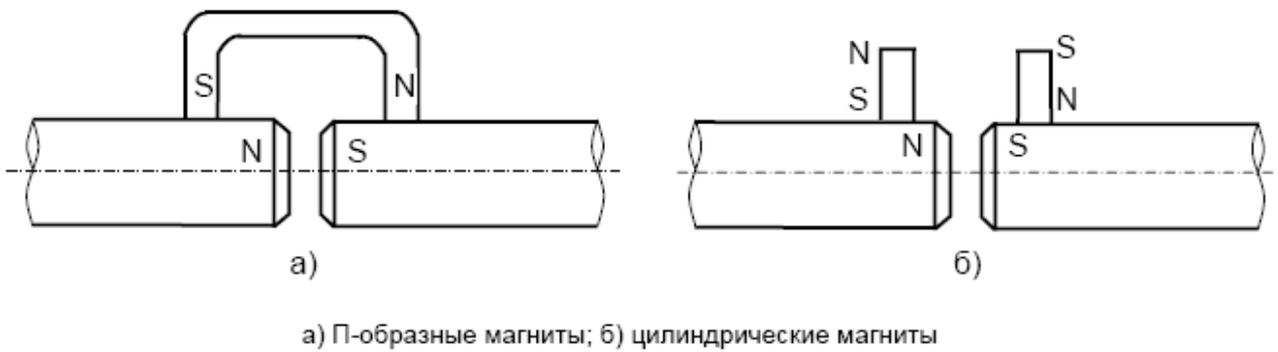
Схема размагничивания сварных соединений постоянными магнитами
